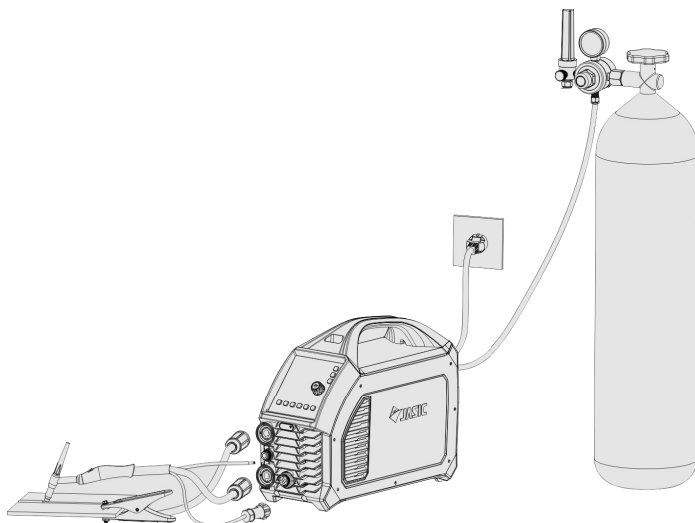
Подключение сварочной горелки, кабеля заземления и газового баллона
